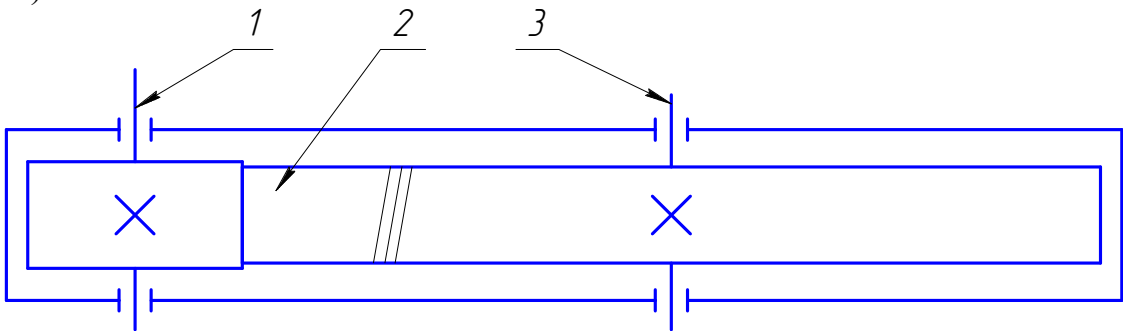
Кінематична схема редуктора: 1 – швидкохідний вал; 2 – зубчаста передача; 3 – тихохідний вал
